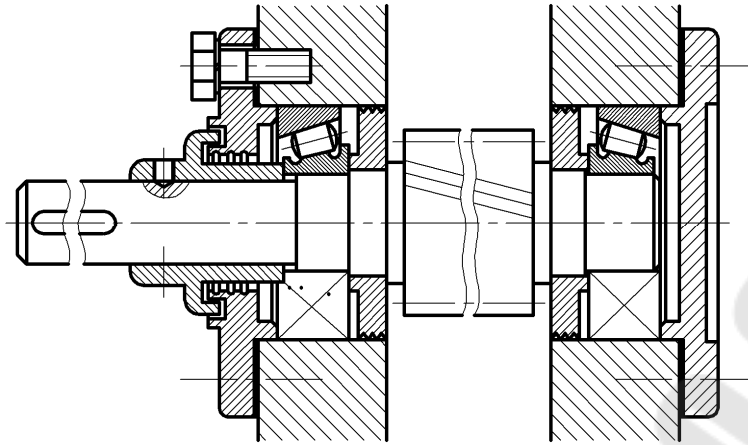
Подшипниковый узел с коническими роликоподшипниками, установленными «враспор» (смазка консистентная)
